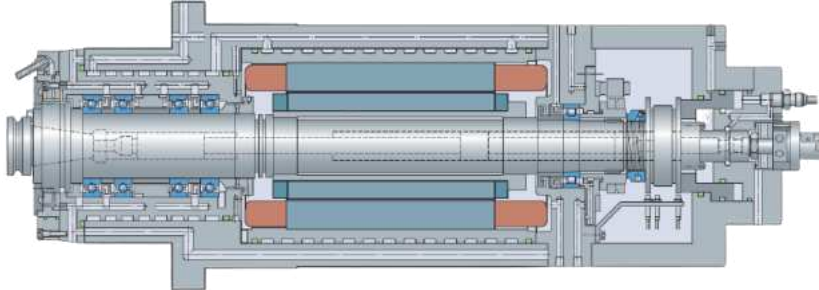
AP utilizat pentru centre de prelucrat CNC cu motor încorporat [53]
